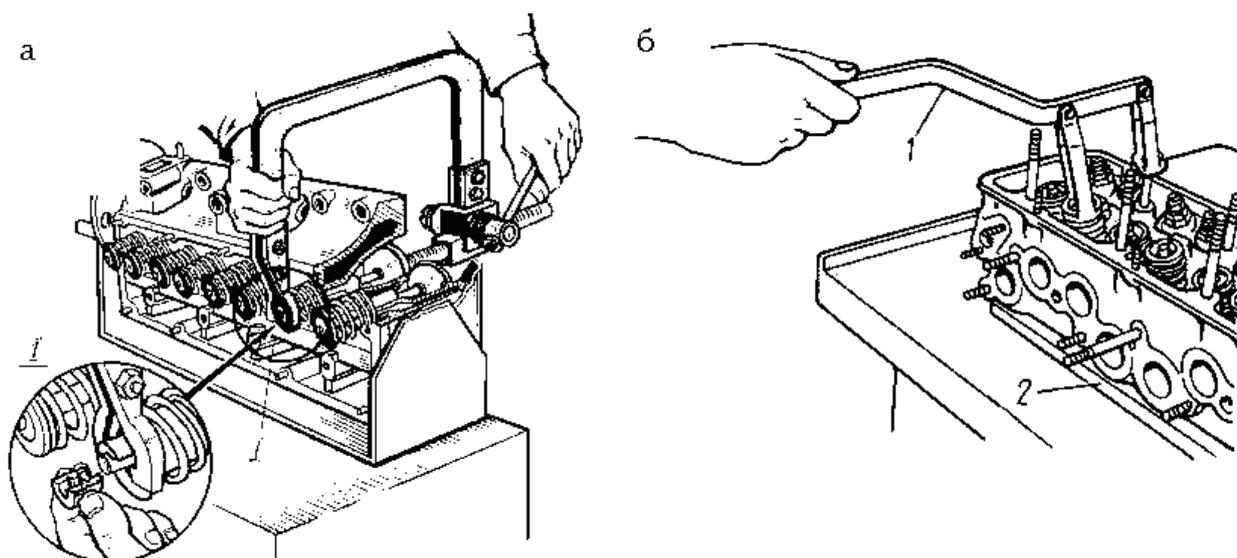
Разборка головки блок цилиндров двигателей «ЗиЛ-130 (а)» и «ВАЗ (б)»: 1-приспособление для снятия клапанов; 2-основание для ограничения движения клапанов
